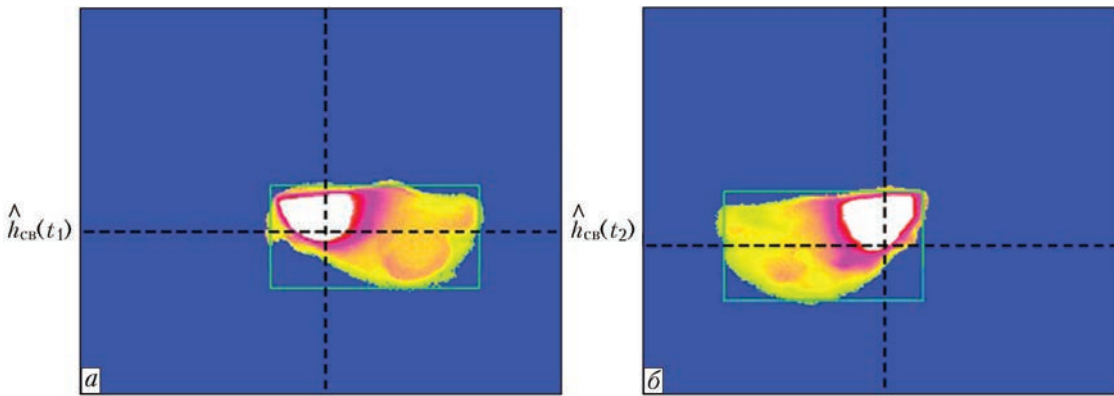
Изображение теплового поля сварочной ванны при сварке корневого шва с поперечными колебаниями: а, б — крайнее левое и крайнее правое положение относительно оси стыка
